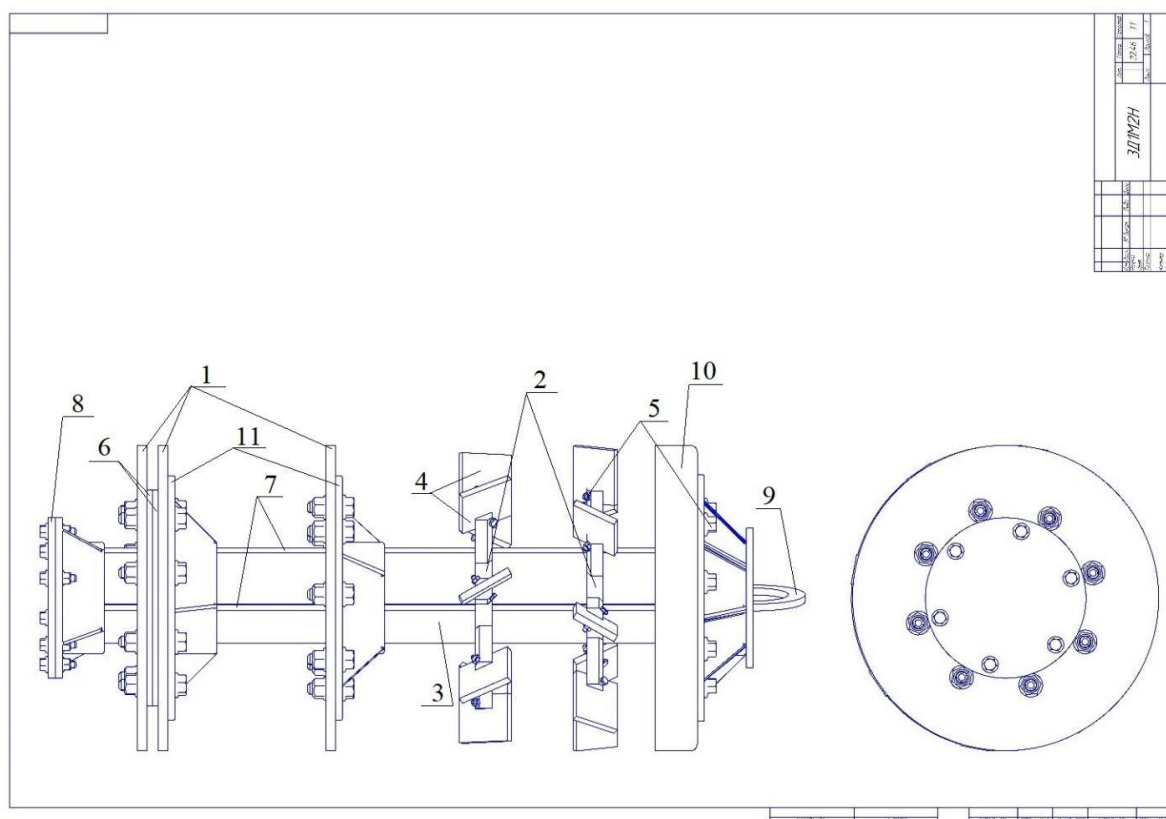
Очистное 3Д1М2Н (вид сбоку): 1 – очистные диски; 2 – блок ножей; 3 – корпус; 4 – ножи для резания парафина; 5 – крепежные элементы; 6 – проставки; 7 – направляющие; 8 – крышка корпуса; 9 – проушина для извлечения ОУ; 10 – очистная манжета; 11 – диски крепления очистных элементов
